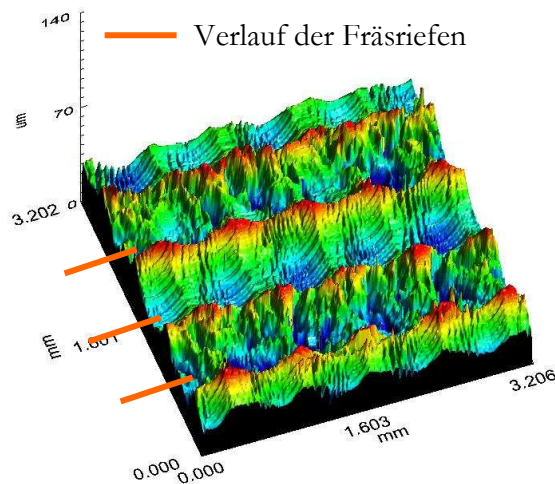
Topographie der mit Kugelfräser Ø12 mm und Zeilensprung 0,8 mm gefrästen Probe aus Material 1.2358
